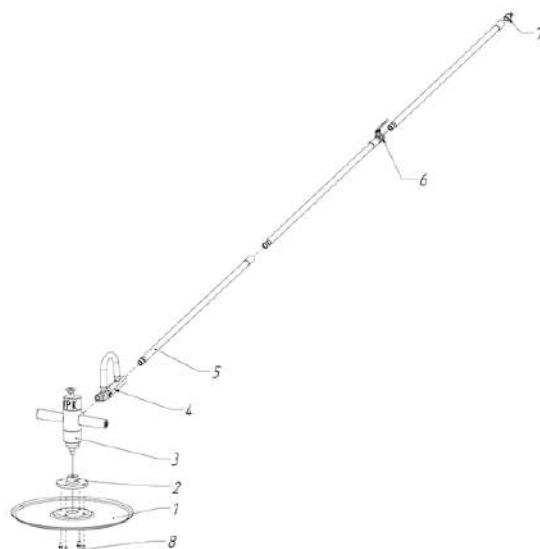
Схема сборки пневматической затирочной машины VPK ПЗМ – 450: 1 – затирочный диск, 2 – фланец, 3 – корпус, 4 – кардан, 5 – рукоять, 6 – кран, 7 – штуцер быстросъемный, 8 – комплектный крепеж.
